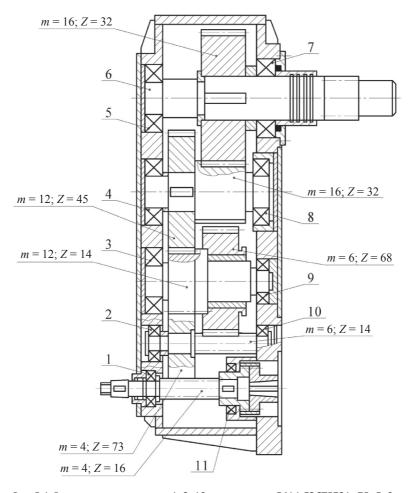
Редуктор привода хода: 1, 2, 10 – подшипник 3614 ГОСТ5721–75; 3, 9 – подшипник 3524 ГОСТ 5721–75; 4, 5, 8 – подшипник 3528 ГОСТ 5721–75; 6 – вал; 7 – подшипник 3538 ГОСТ 5721–75; 11 – подшипник 124 ГОСТ8338–75
